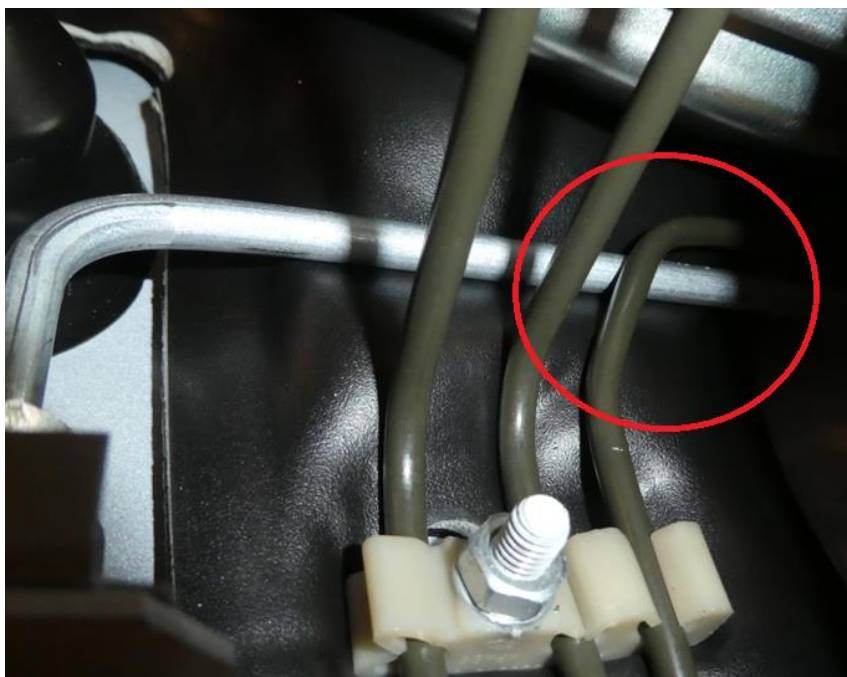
Контакт тормозной трубки и трубки сцепления
